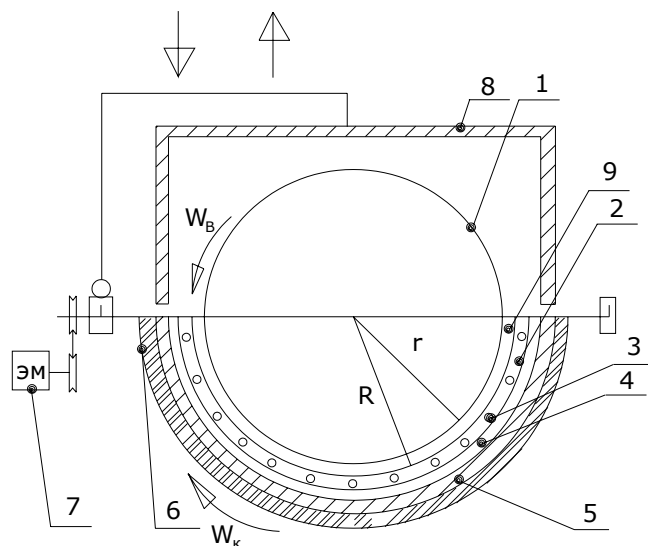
Схема поперечного сечения установки для изготовления параболических и конусообразных отражателей солнечной энергии. 1 – профилированный формующий вал; 2 – форма для отражателя; 3 – электронагреватели; 4 – каналы охлаждения водой; 5 – теплоизоляция; 6 – движущаяся каретка; 7 – электродвигатель; 8 – теплоизолированный колпак; 9 – изготавливаемый отражатель.
